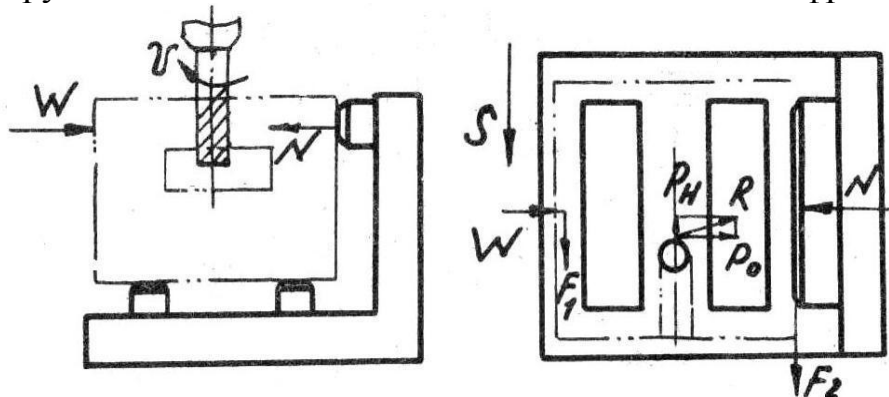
Схема розрахунку сил затиску для фрезерування кінцевою фрезою
